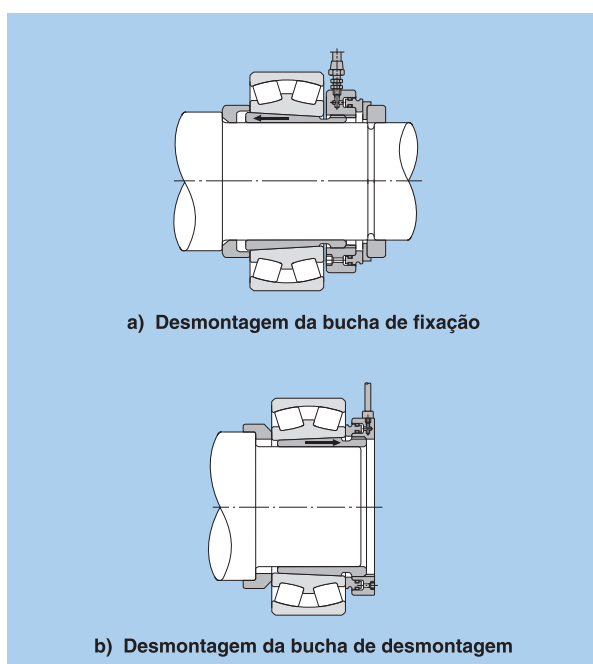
Desmontagem utilizando uma porca hidráulica
